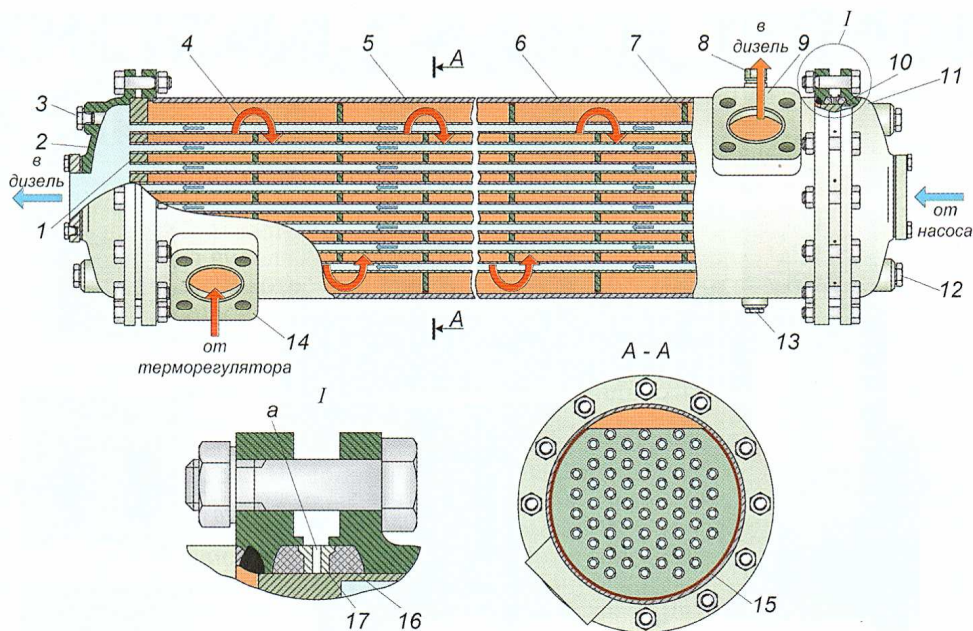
Водомасляный теплообменник: 1, 10 — трубные доски; 2, 11 — крышки; 3, 8, 12, 13 — пробки; 4 — трубки; 5, 6 — корпус; 7 — перегородка; 9, 14 — патрубки; 15 — наполнитель; 16 — уплотнительное кольцо; 17 — промежуточное кольцо; а — контрольное отверстие
